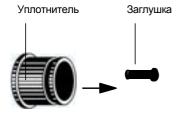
Извлечение заглушки с конца уплотнителя
